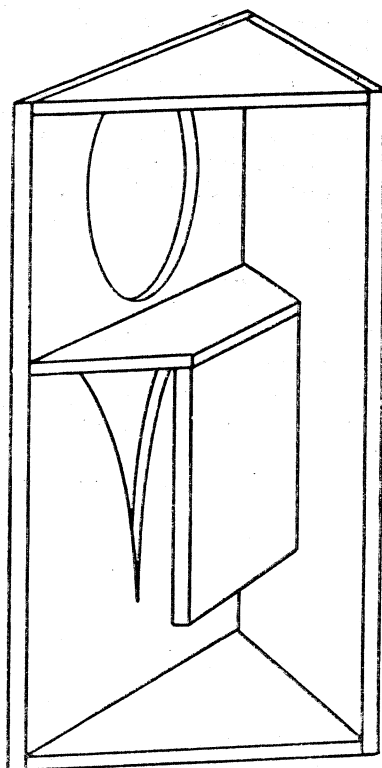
Vista de frente e cortes do móvel já pronto.
